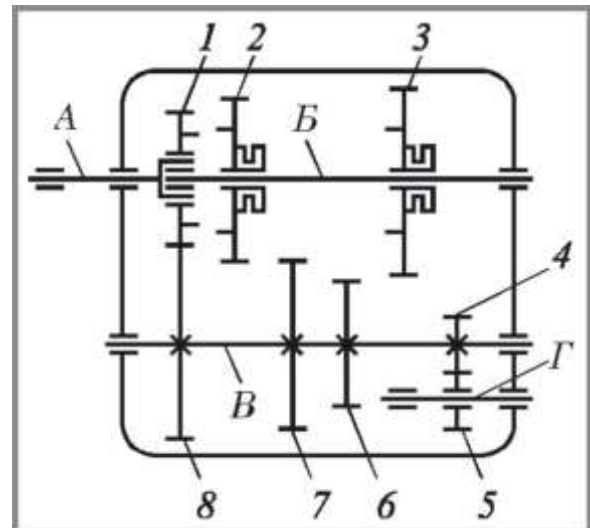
Схема триступінчастої коробки передач: *A* – ведучий вал; *B* – ведений вал; *B* – проміжний вал; *Г* – вісь зубчастого колеса передачі заднього ходу; *1* – *8* – зубчасті колеса
